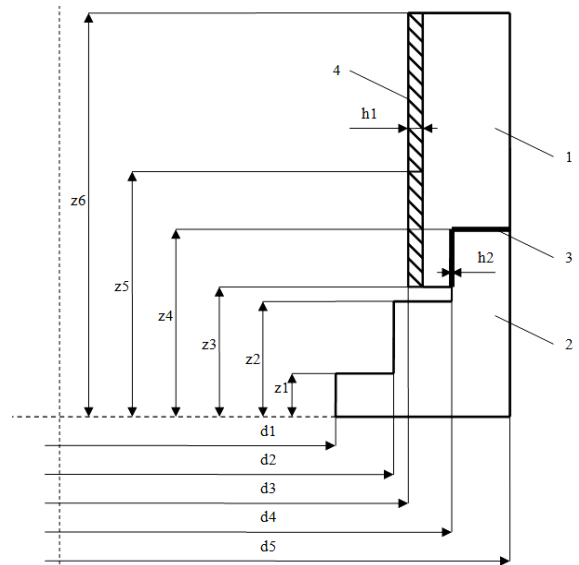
Схема поперечного перерізу паяного корпусу гідроциліндра:
